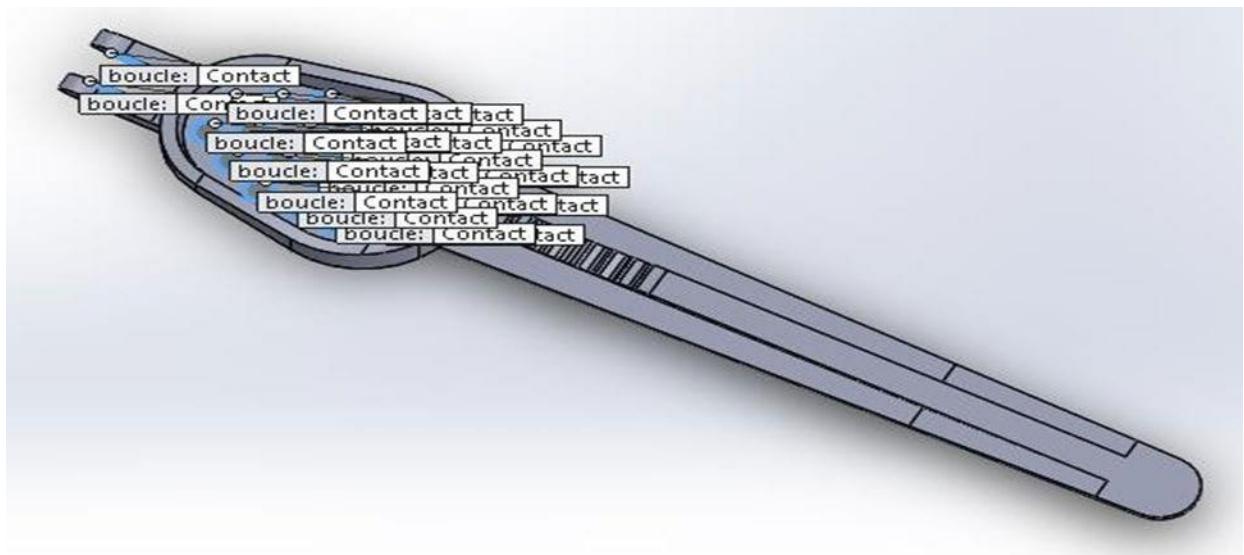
Surfaces d'arrêt de la pièce bas.
